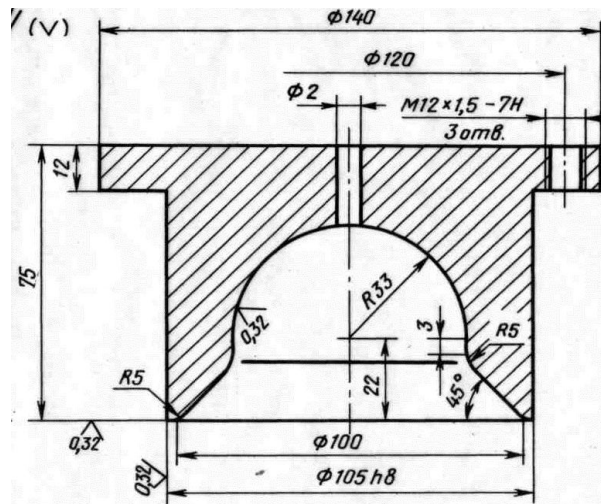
Типовая конструкция матрицы для вытяжки пластичным металлом
